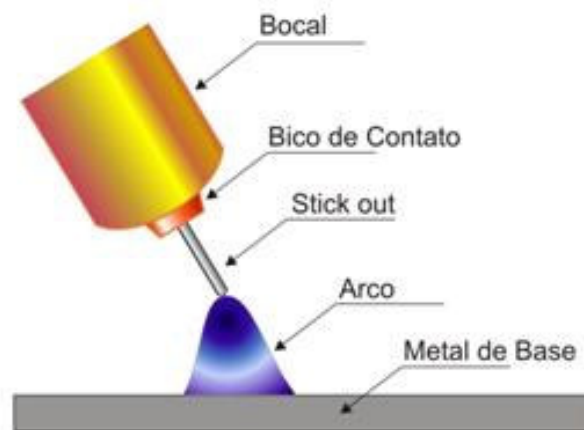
Nomenclatura utilizada na soldagem MIG/MAG
